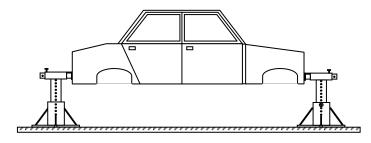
Расположение несущего кузова автомобиля в кантователе
